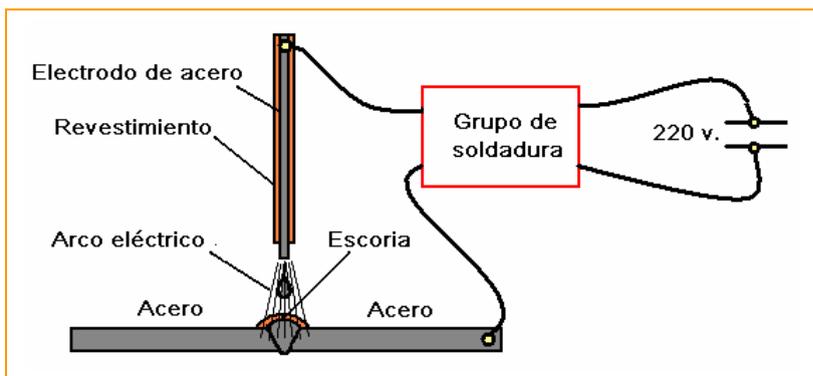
Soldadura por arco manual en electrodos revestidos.
